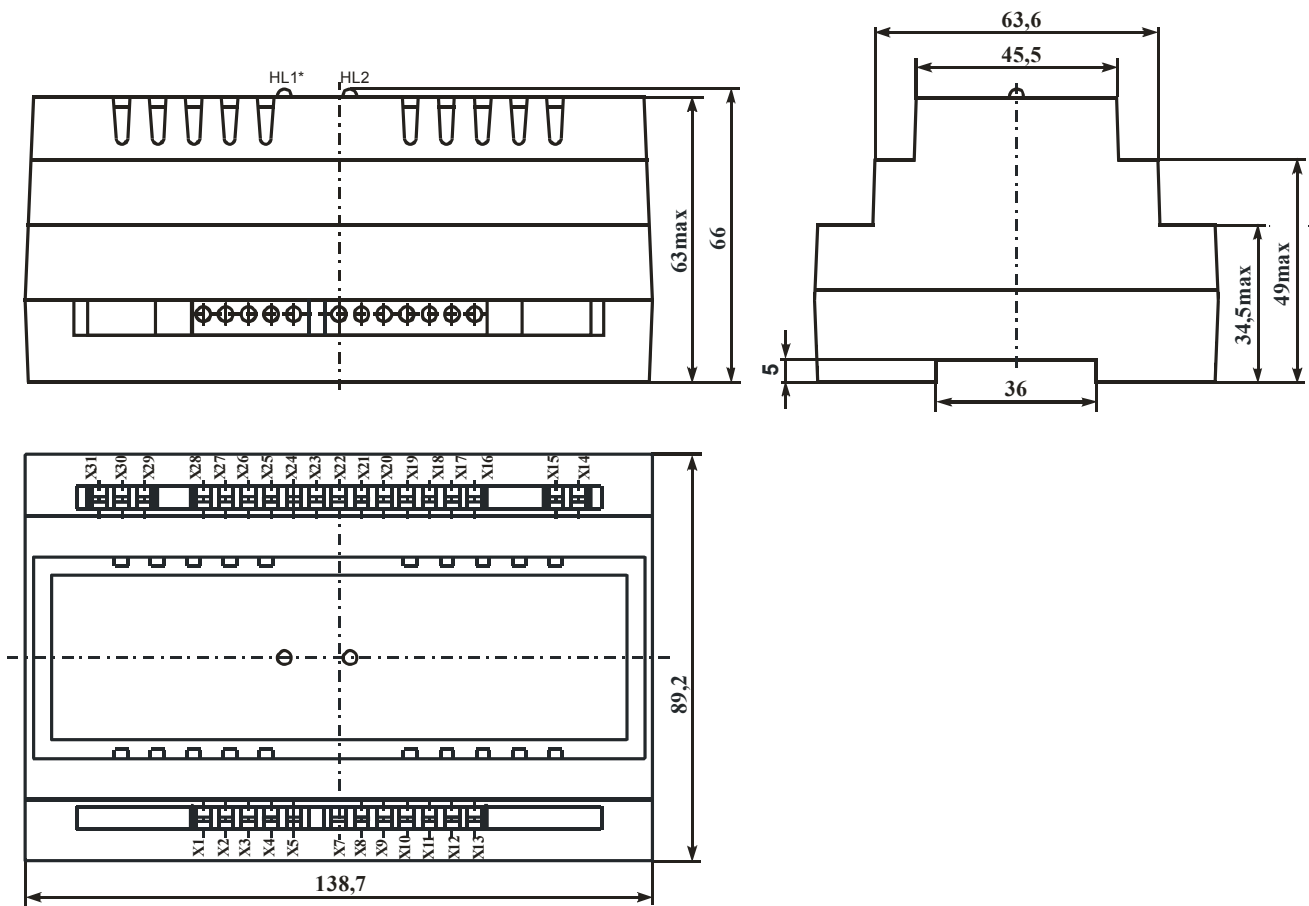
Габаритный чертеж - исполнение 1
